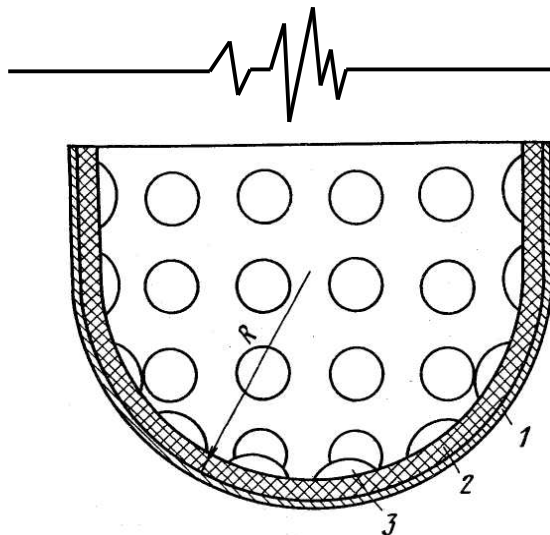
Рабочая камера для виброударной обработки (поперечное сечение) [26]:
